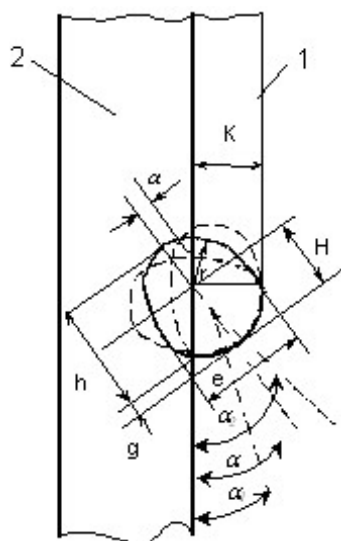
Сечение углового шва: 1 – металл M1; 2 – металл M2; e – ширина шва; g – высота выпуклости;  $a = d_{\text{эл}}$  – диаметр электродной проволоки; г – радиус; K – катет шва; h – глубина проплавления; H – высота жидкого металла сварочной ванны
